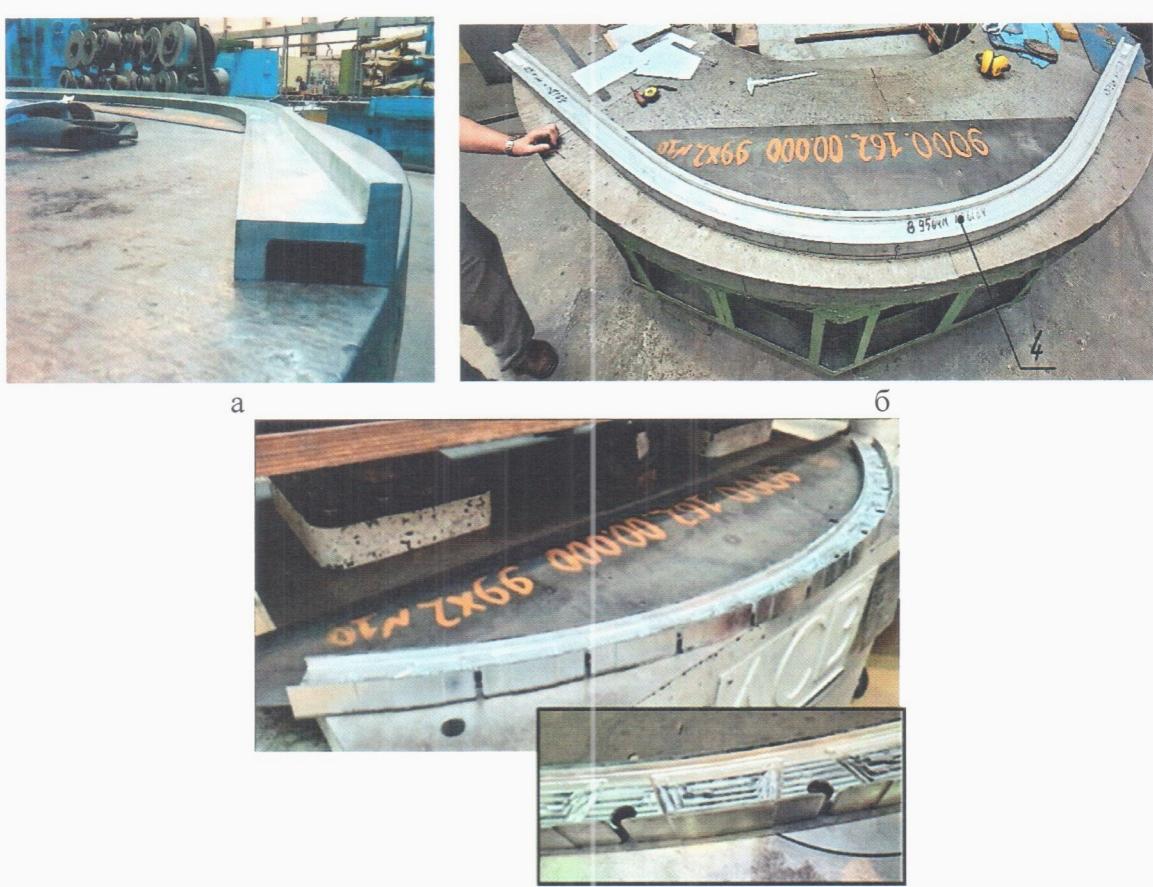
Внешний вид формообразованного прессованного профиля из сплава В95оч (а, б) и сегмента шпангоута из него (в)
